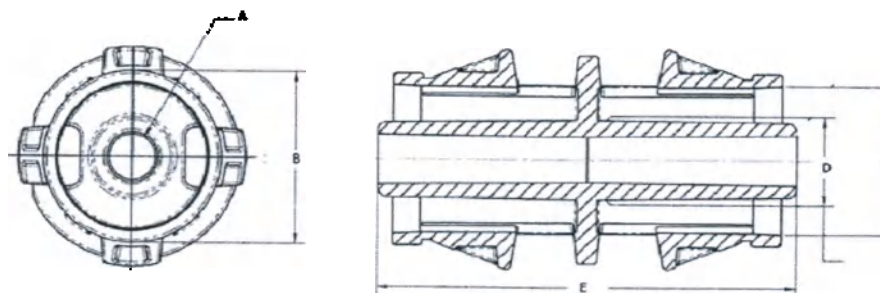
Соединитель прямой TRUE-LOCK, общий вид / Figure 11 –TRUE-LOCK Connector straight, general view
